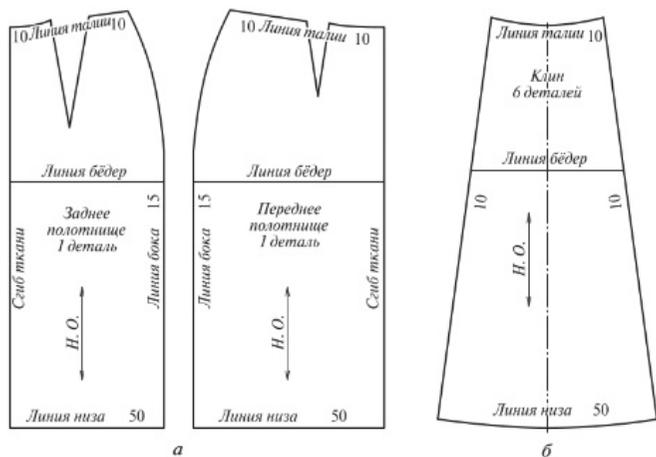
Детали выкройки юбок: а — оформление выкройки прямой юбки; б — оформление выкройки клинковой юбки
